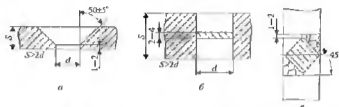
Схема подготовки отверстия под заварку зенкованием (а); схема подготовки отверстия под заварку установкой перегородки (б); схема заварки отверстия с помощью установки пробки (е); 1—5 — последовательность наложения слоев
